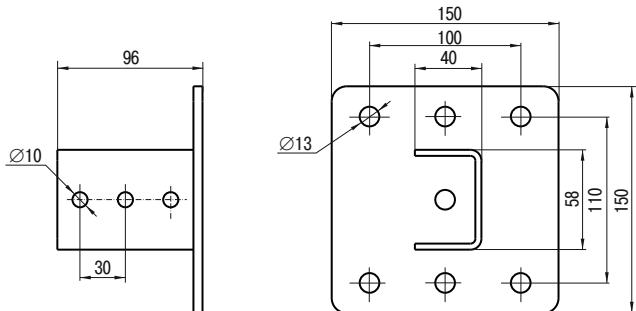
Крепление потолочное для П-образного профиля / Figure 2. Ceiling mounting fitting for U-shaped profile
